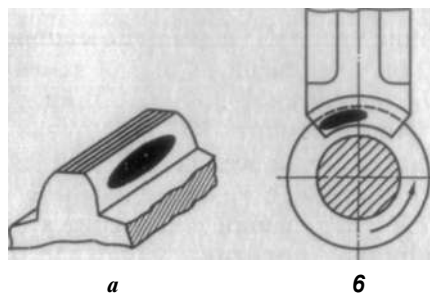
Размещение пятна контакта цилиндрической (а) и червячной (б) передач
